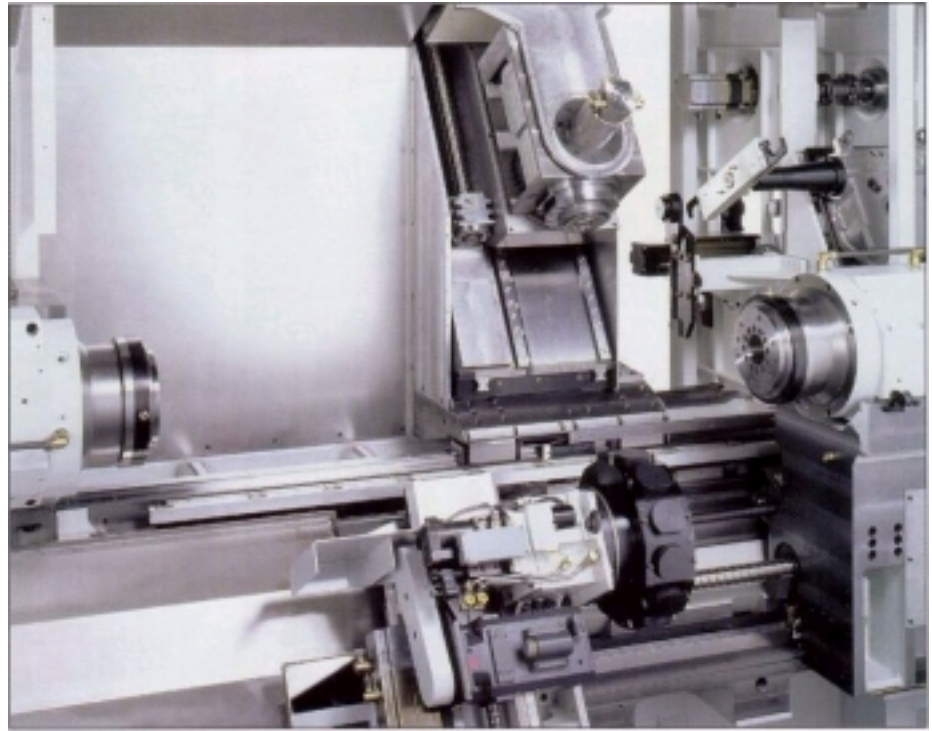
, vielseitig: Die beiden Drehspindeln und die Dreh-Frässpindel auf dem YS-Schlitten ermöglichen komplexe 6-Seiten-Bearbeitung
